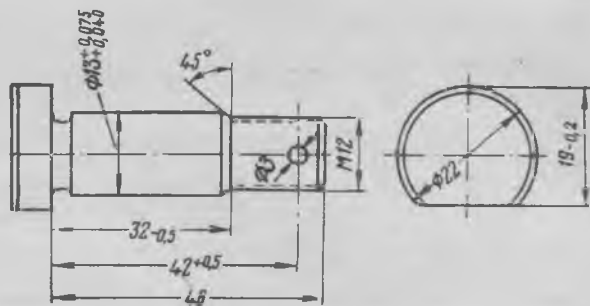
Призонный болт крепления насосных колес гидромуфт
